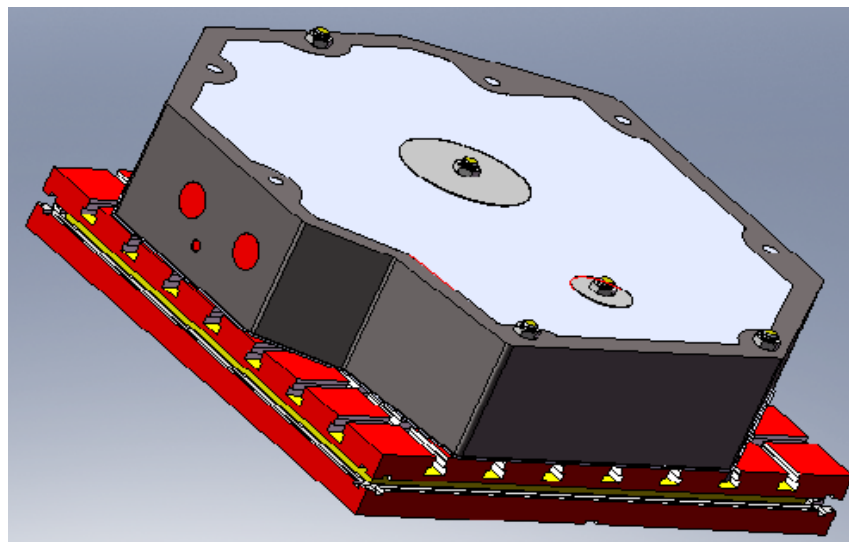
Зовнішній вигляд пристосування для обробки деталі типу «Корпус».
